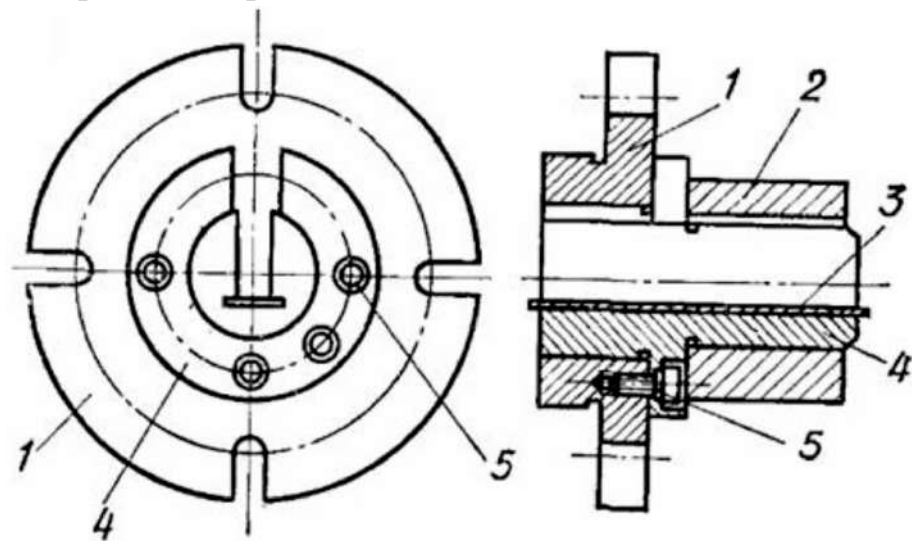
Пристрій для протягування шпонкових пазів в отворах
